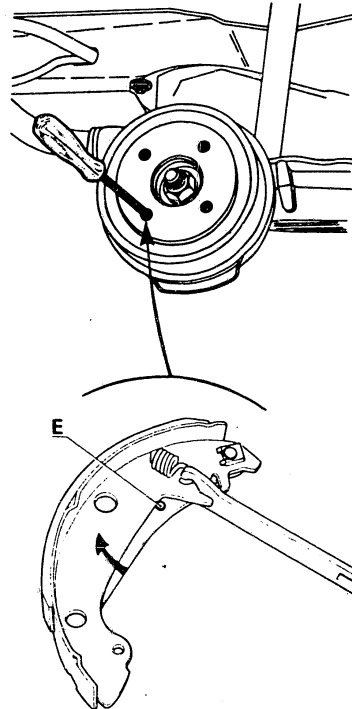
Trommeldemontage: Mit einem Schraubenzieher wird der Handbremsbetätigungshebel nach innen gedrückt. Erst dann lässt sich die Trommel leicht wegnehmen.
